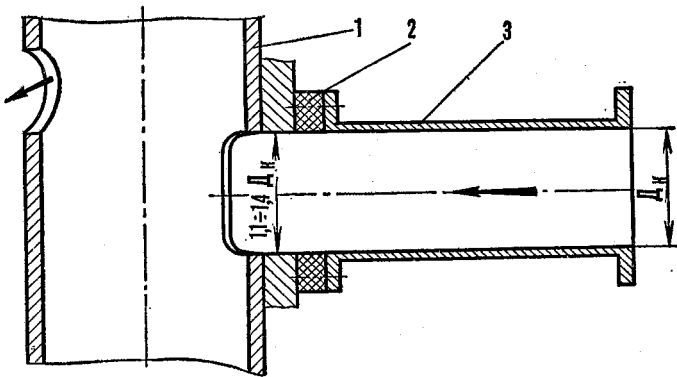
Впускной патрубок: 1 — гильза цилиндра; 2 — теплоизолирующая прокладка; 3 — патрубок; D_k — диаметр диффузора-карбюратора
